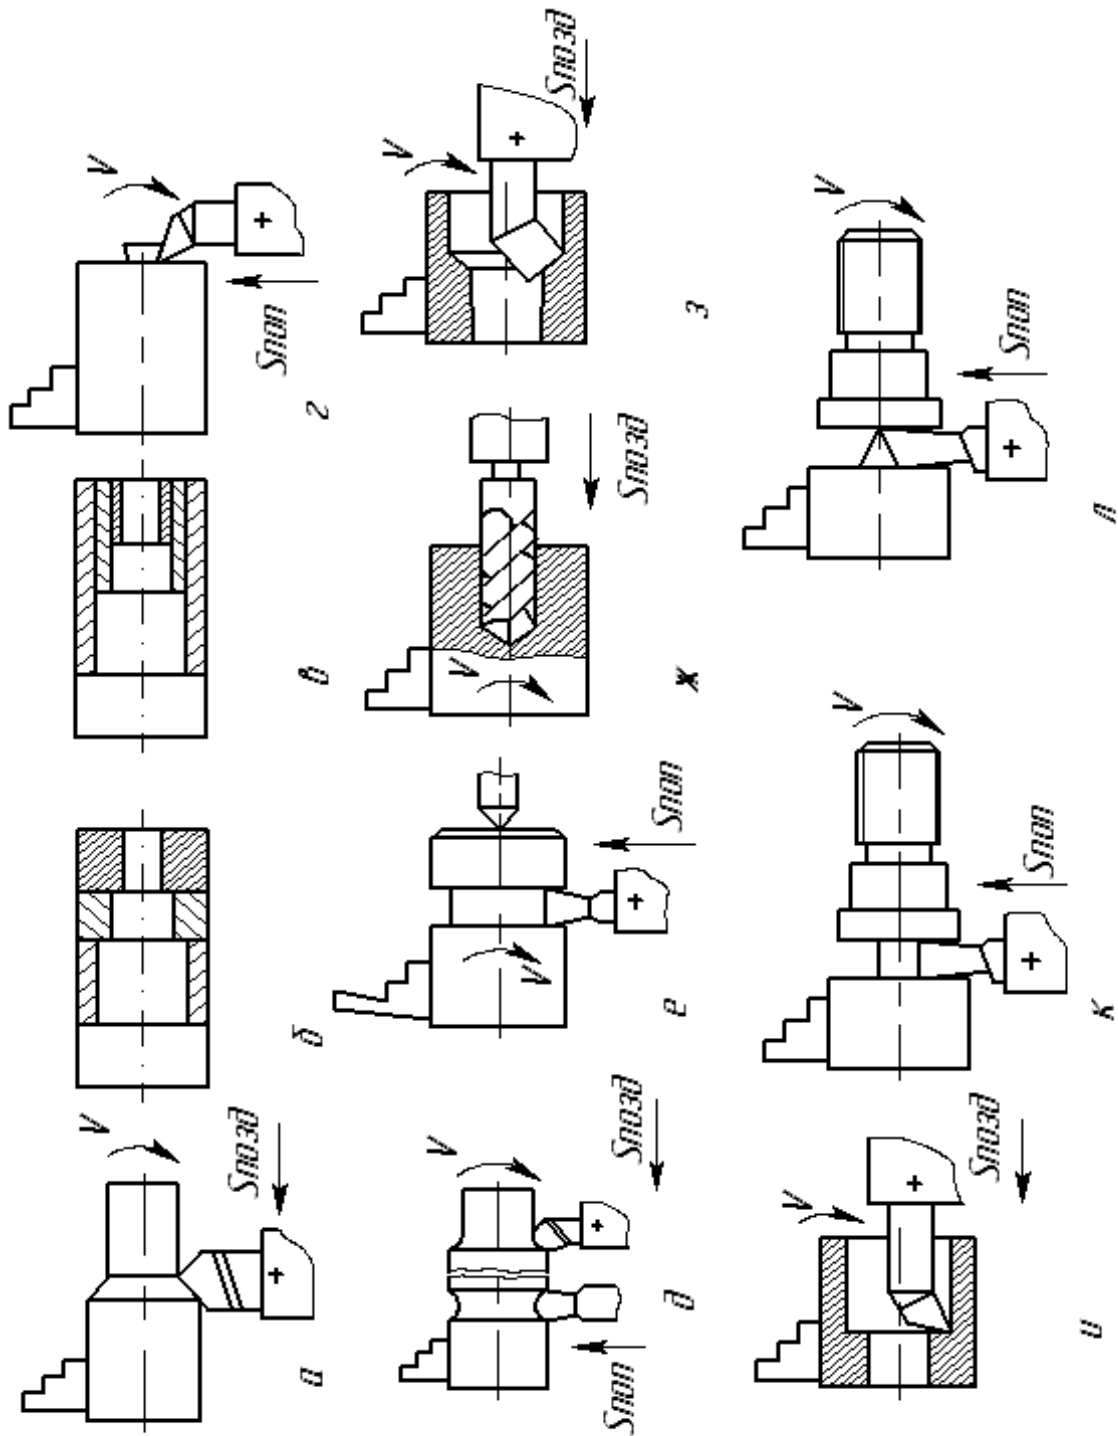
Схеми обробки заготовок на токарно-гвинторізних верстатах
